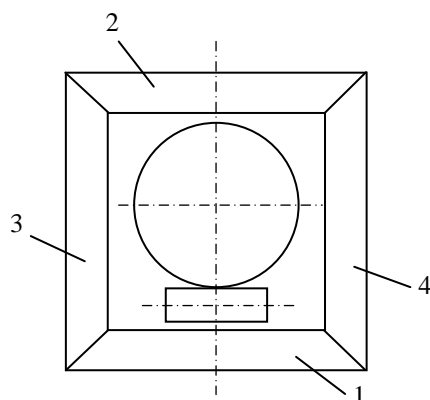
П7 Варианты присоединения лап в редукторе Ч-80:
